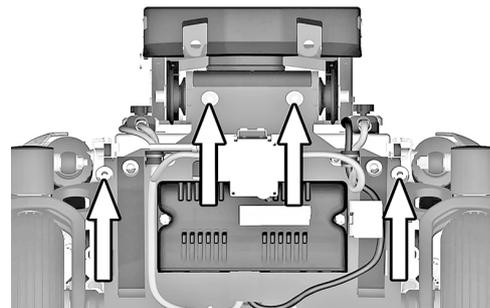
La caja de las baterías está asegurada con cuatro pernos.
